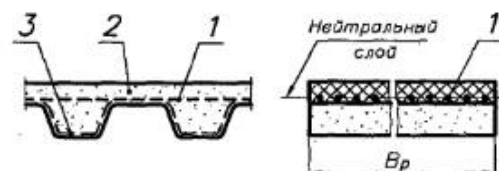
Конструкция зубчатого ремня с трапецидальными зубьями: 1 - кордшнур (металлокорд или углеродное волокно); 2 - тело ремня (маслостойкая резина, пластмасса); 3 - тканевая обкладка (для ремней, изготовляемых методом прессования)
